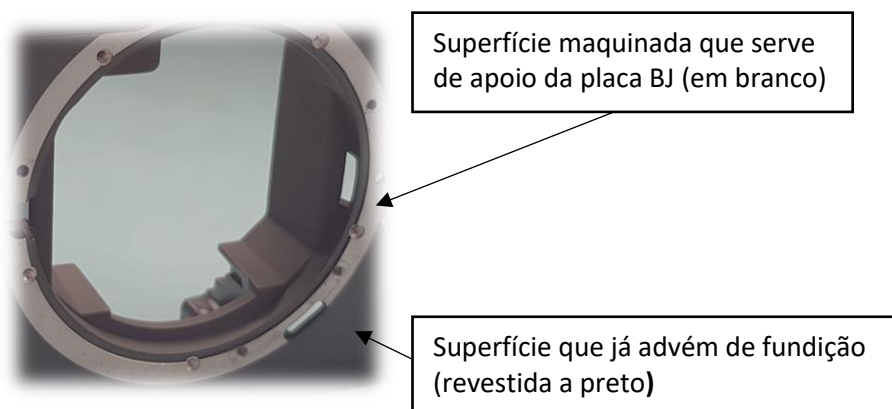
Corpo principal, identificação da superfície de apoio da placa BJ
